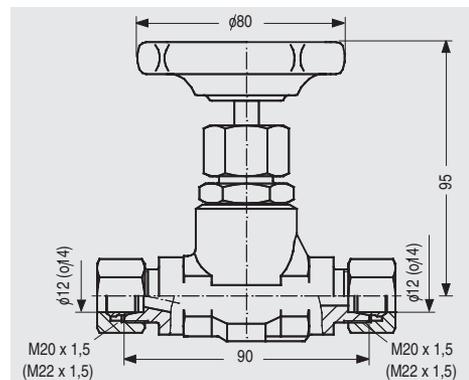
/134 Запорный вентиль 7MF9017-1C, -1D, -2C, -3C, размеры
